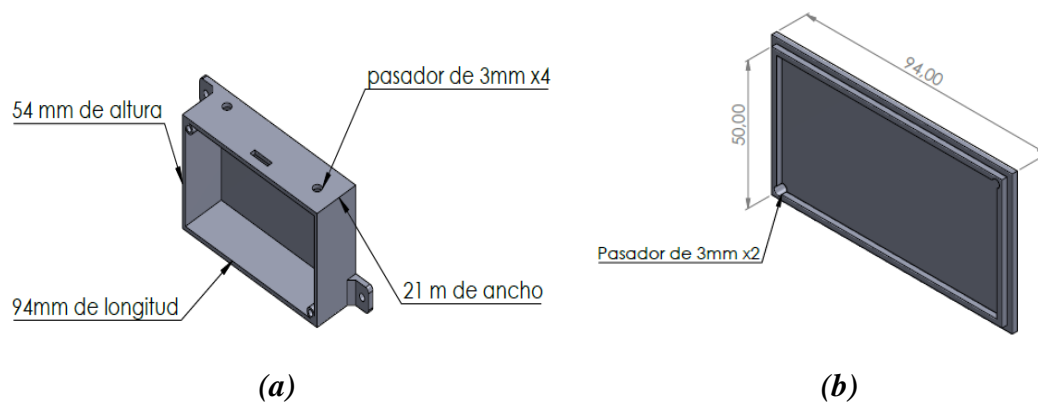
Carcasa protectora, (a) vista isométrica caja, (b) vista isométrica tap
